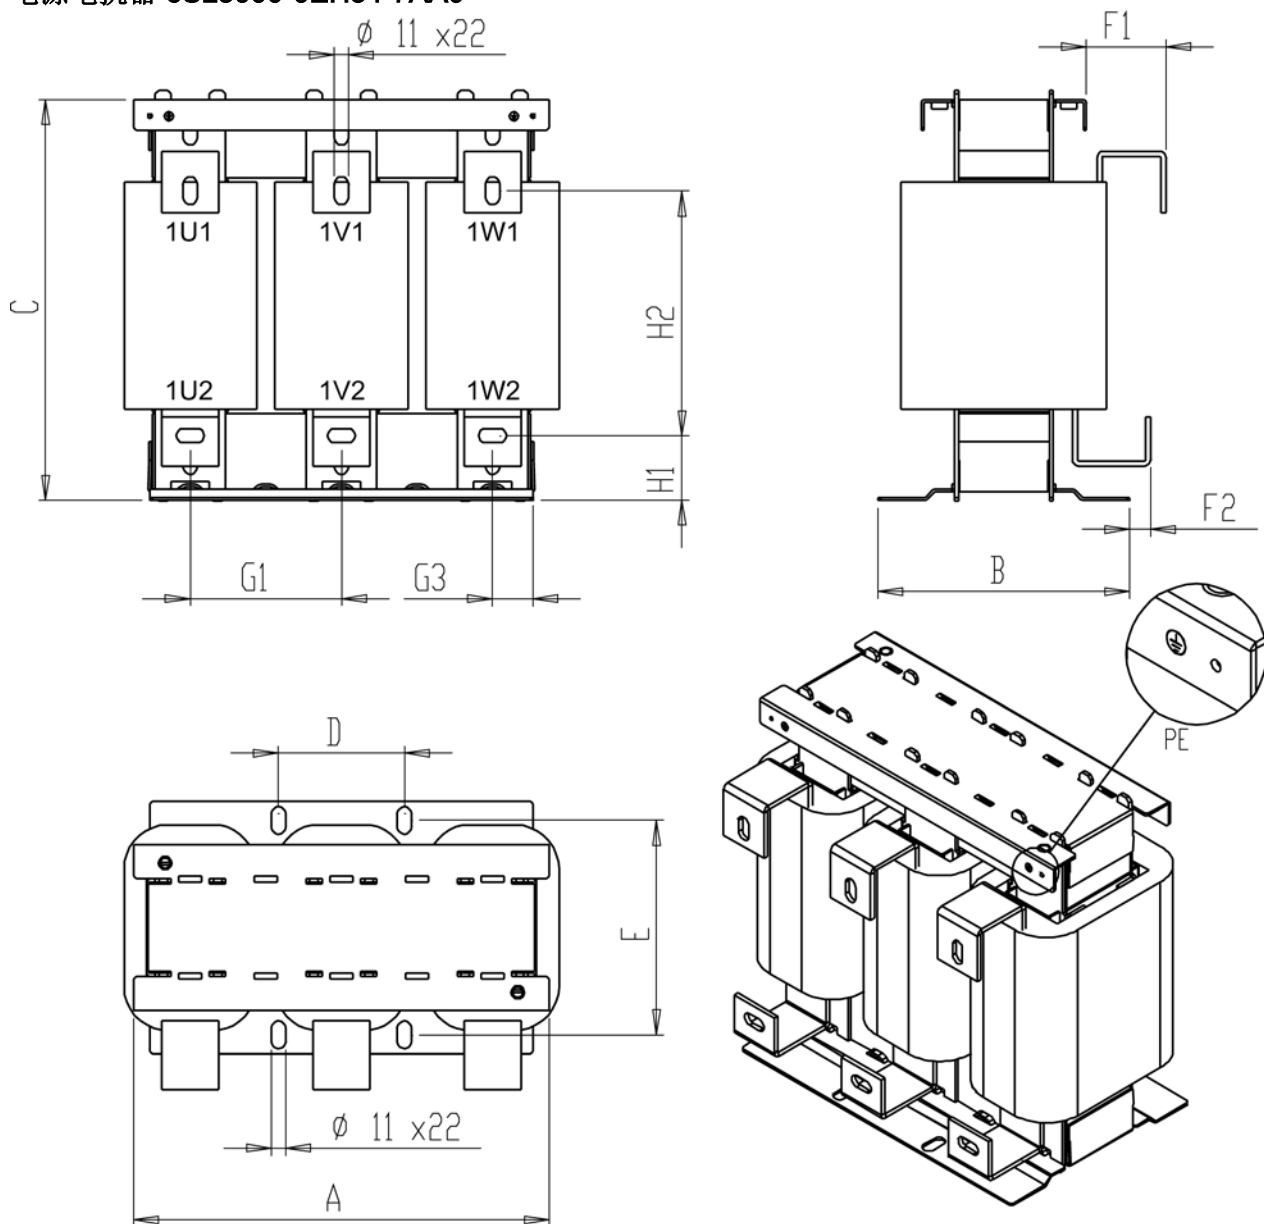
电源电抗器 6SL3000-0EH34-7AA0 的外形尺寸图
